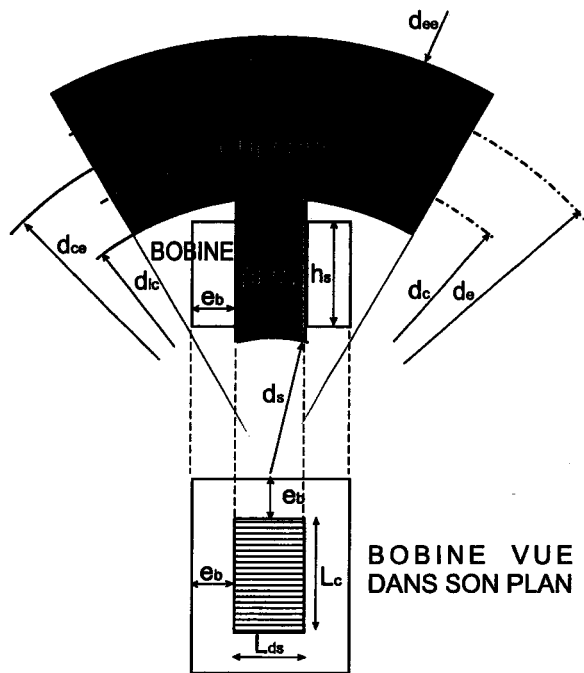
Paramètres dimensionnels du stator et de la bobine pour l'étude thermique et géométrie de la bobine vue dans le plan des enroulements.
